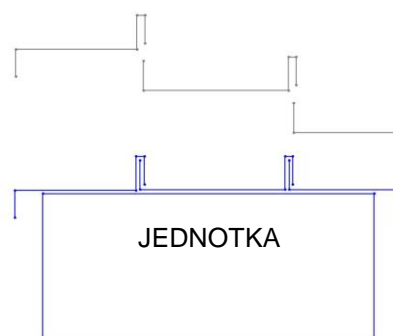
ÚPRAVA PRO VENKOVNÍ PROVEDENÍ - MONTÁŽ STŘECHY
